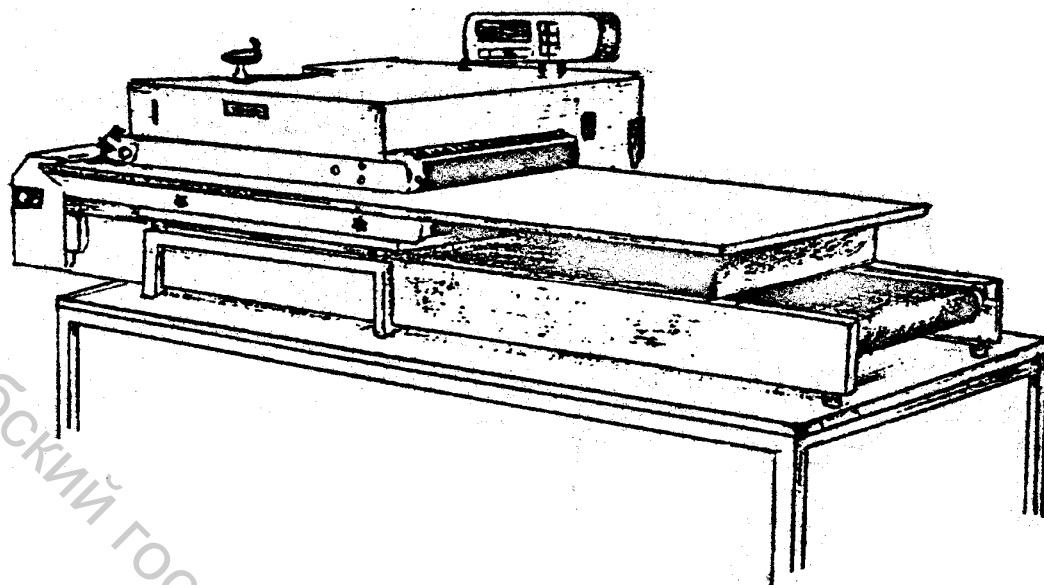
Внешний вид пресса RPS-L фирмы «Майер»
